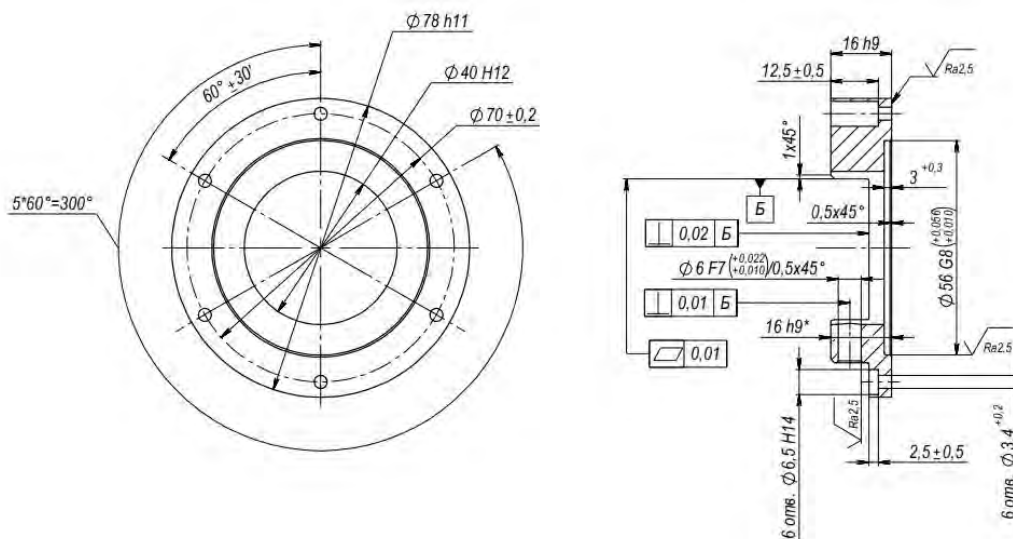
Фрагмент чертежа детали «Проставка поворотная»
